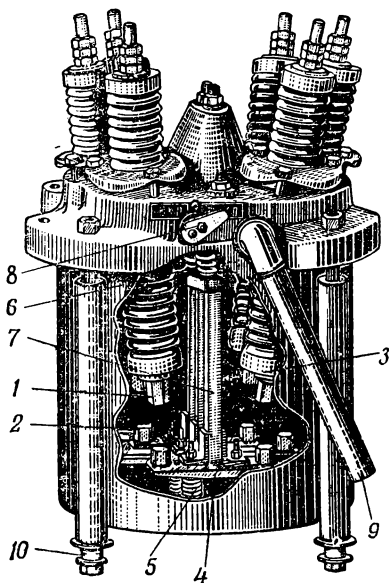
Частичный разрез выключателя типа ВМБ-10.
